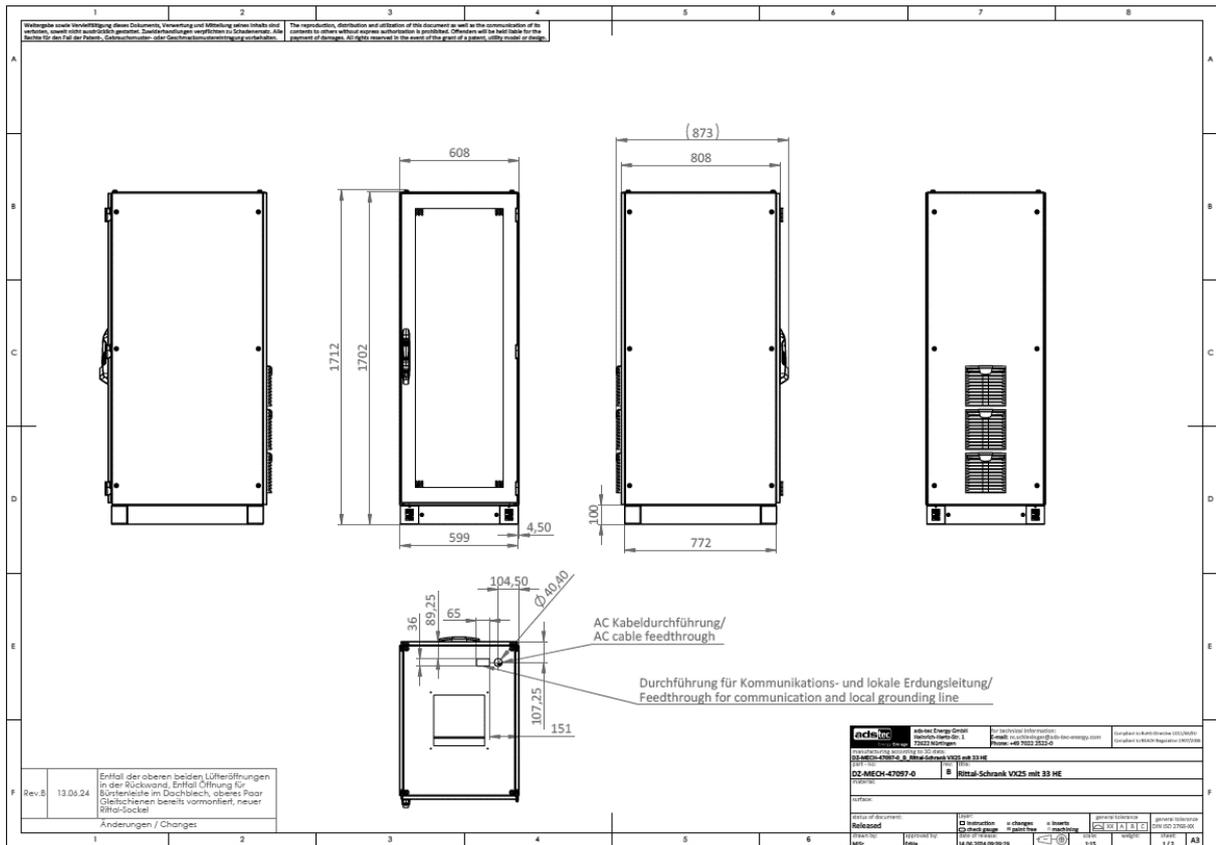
Konstruktionszeichnung Schrankgehäuse V2.0 - Blatt 1
